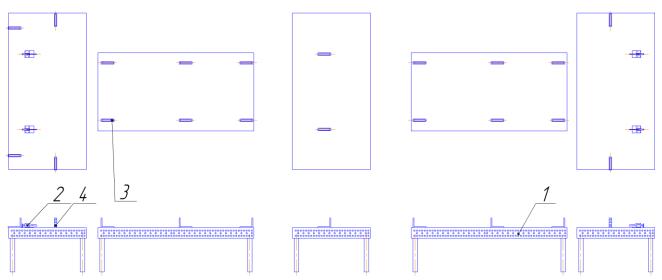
Устройство приспособления сборочно-сварочного $\Phi \mbox{OPA.000001.136.00.000 CF}$
